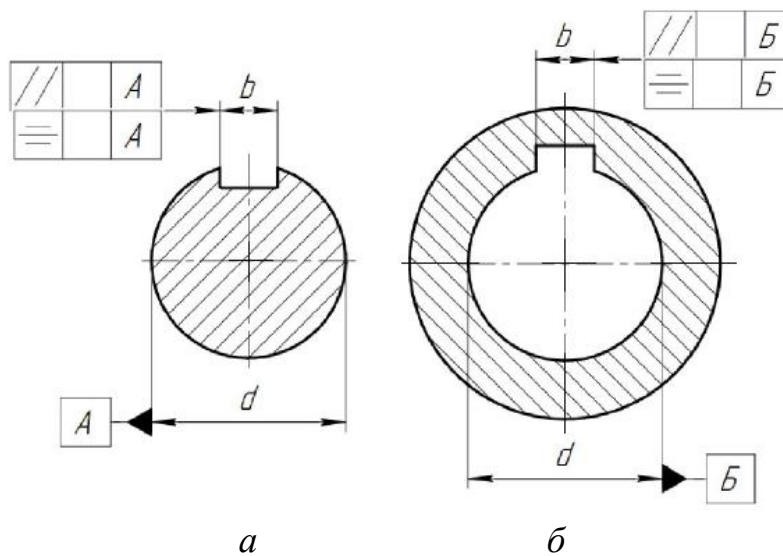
Допуск форми та розташування поверхонь шпонкового паза на валу a та на втулці $б$
